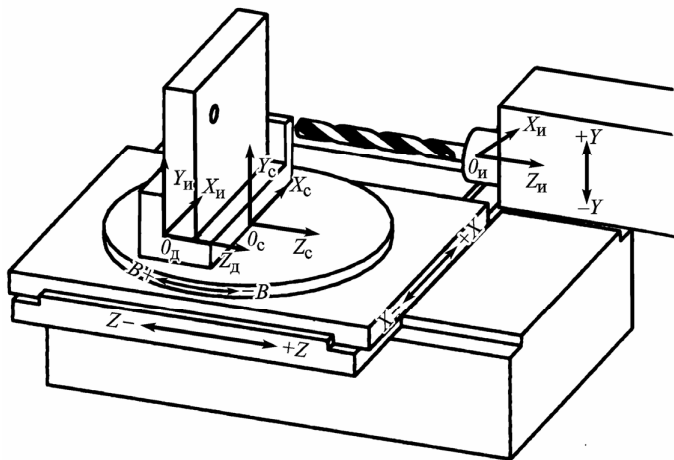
Схема связи систем координат детали и инструмента сверлильно-фрезерно-расточного станка с ПУ
